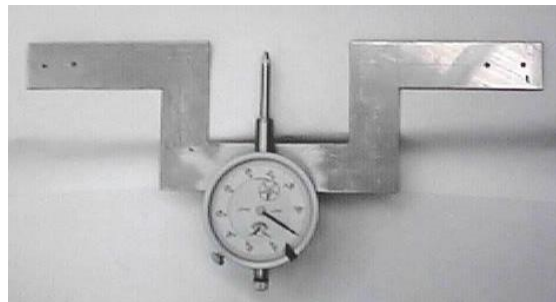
Dispositivo para medir deflexión en el sandwich
